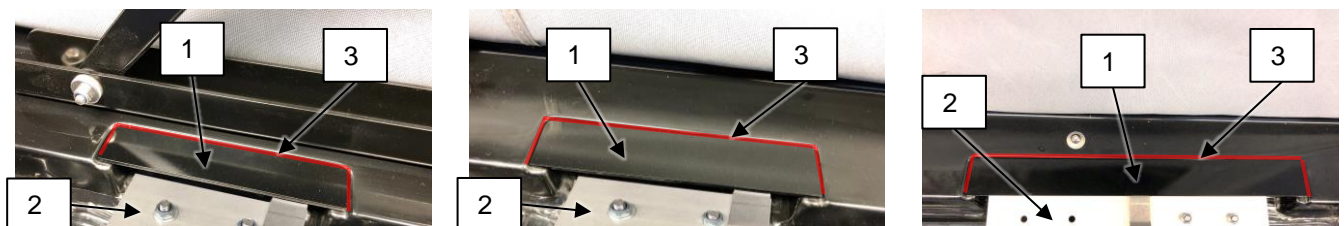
Montage mit Markise / *Assembly with awning
